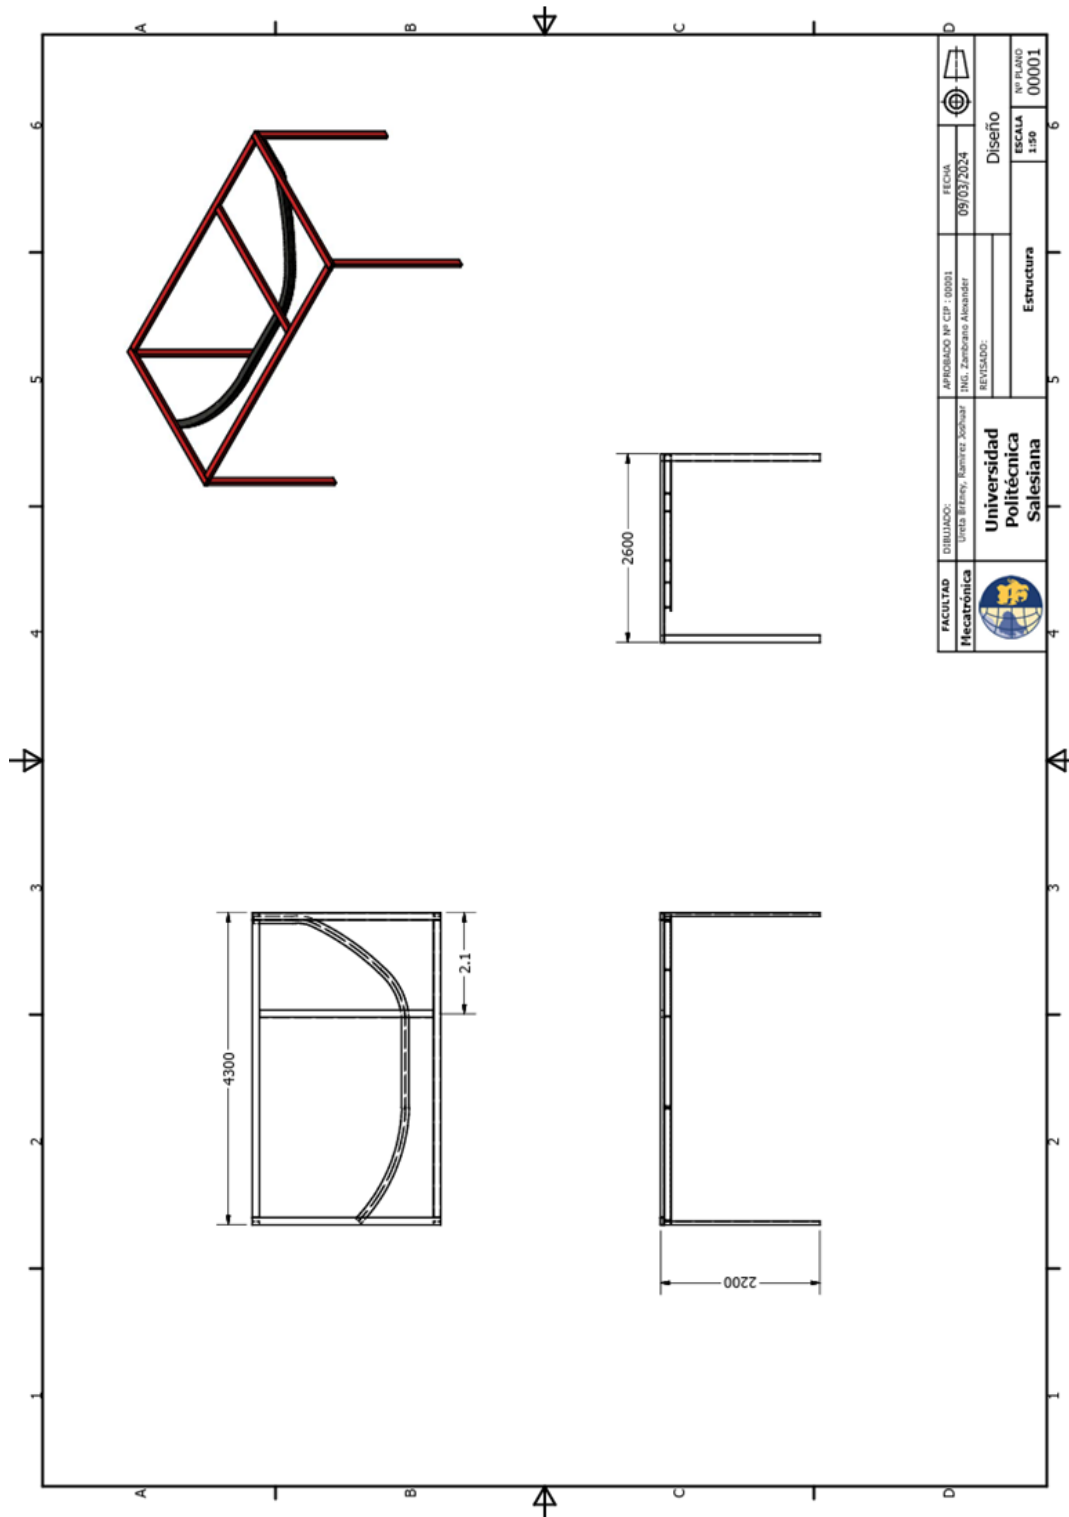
Estructura, Fuente: J.Ramirez, B.Ureta
